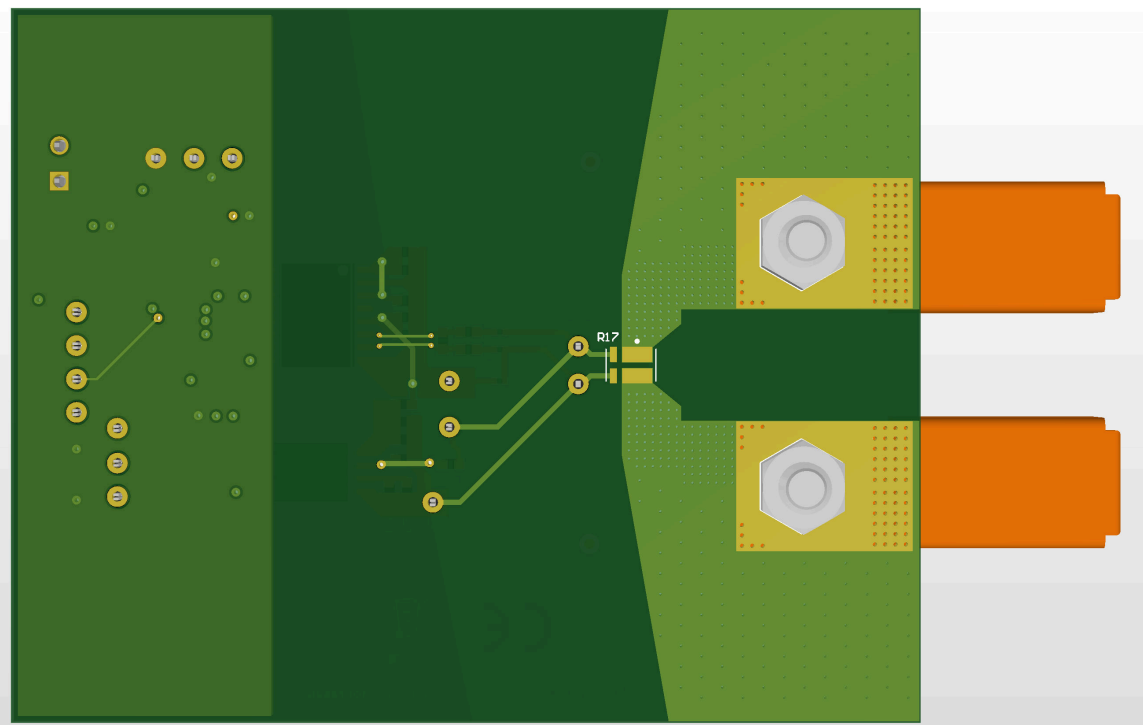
AMC-AMP-50A-EVM 底部 PCB 图
